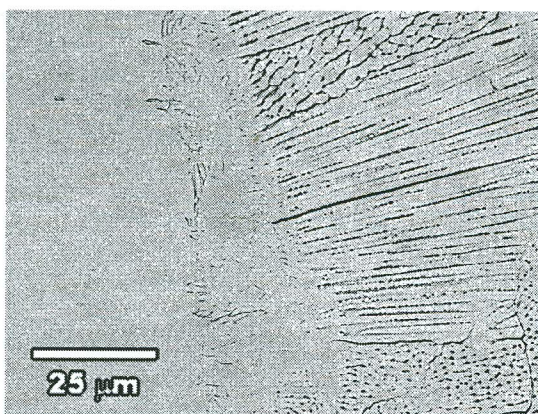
Detalhes do cordão de solda típicos de processo laser da união entre o AISI 304 e o Inconel 600, mostrando a ZF e ZAC (AISI 304 à esquerda e Inconel 600 à direita).
